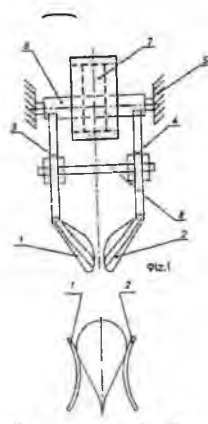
Схема лемішного коливного копача з випуклою формою робочої поверхні коливних лемешів і регульованою відстанню між ними: а-загальна схема копача; б-вид робочих
